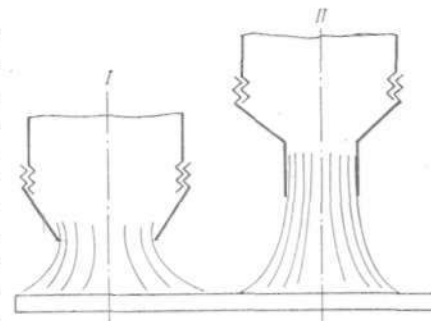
Форма сопел для сварки в среде защитных газов.
